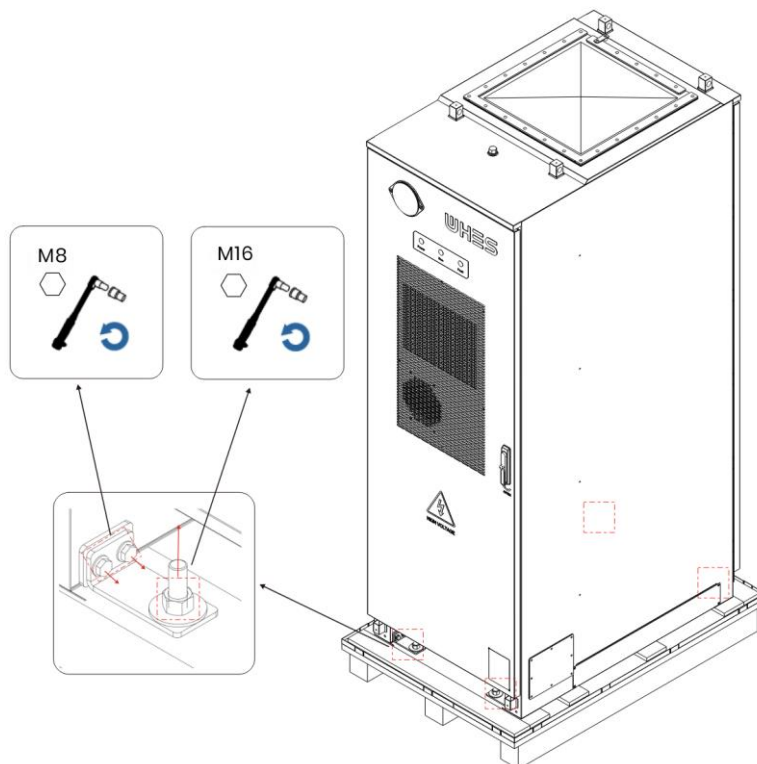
Entfernen der Holzpalette und der Befestigungswinkel
